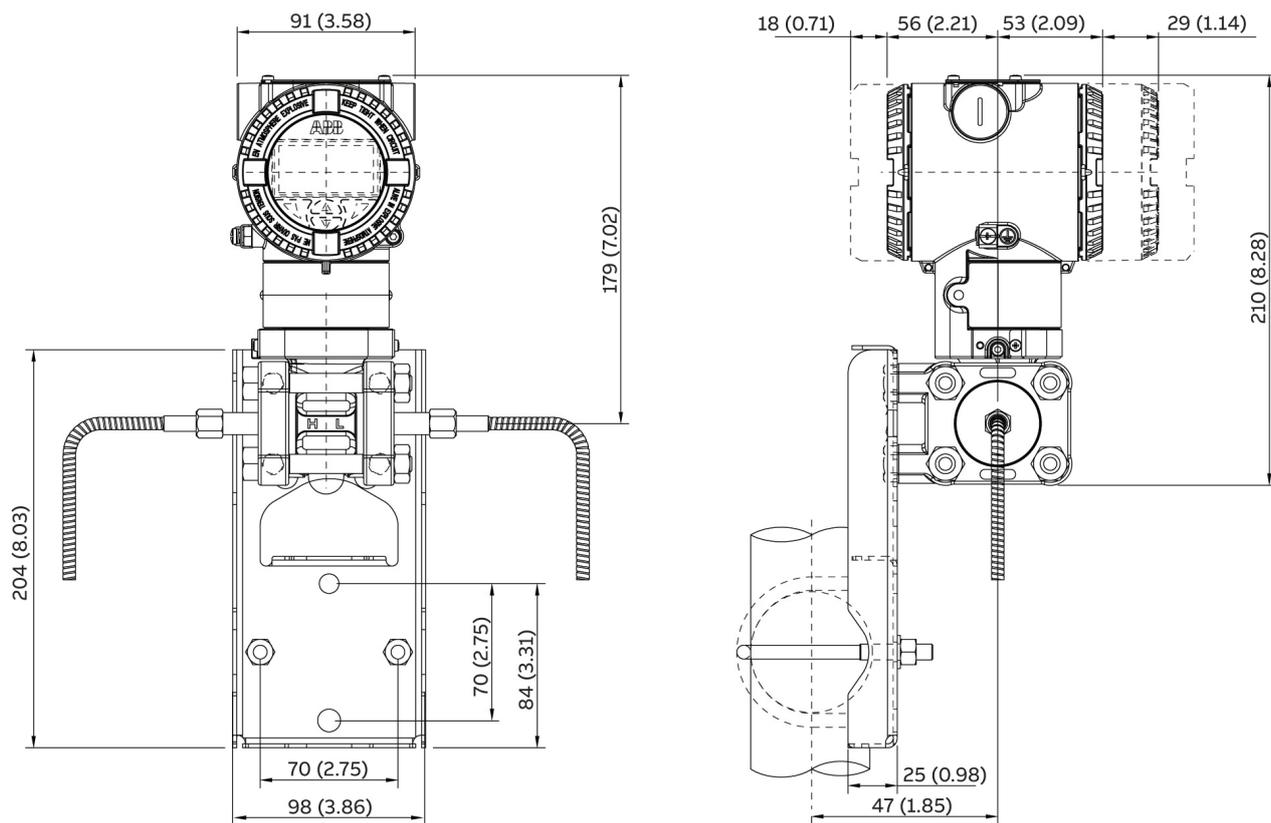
Support plat pour montage sur tuyauterie - boîtier cylindrique
